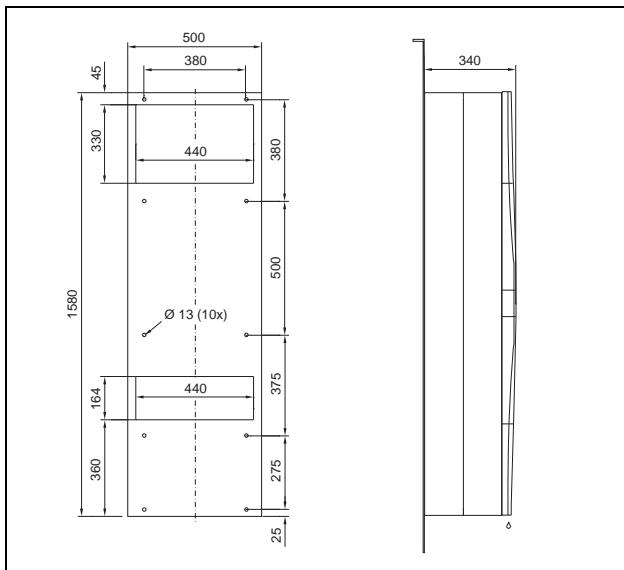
SK 3304.xxx, SK 3305.xxx, pro montáž na povrch
